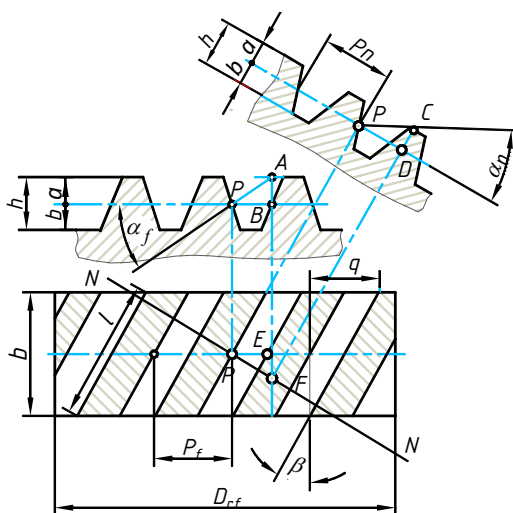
Unghiurile de angrenare în plan frontal și plan normal.
